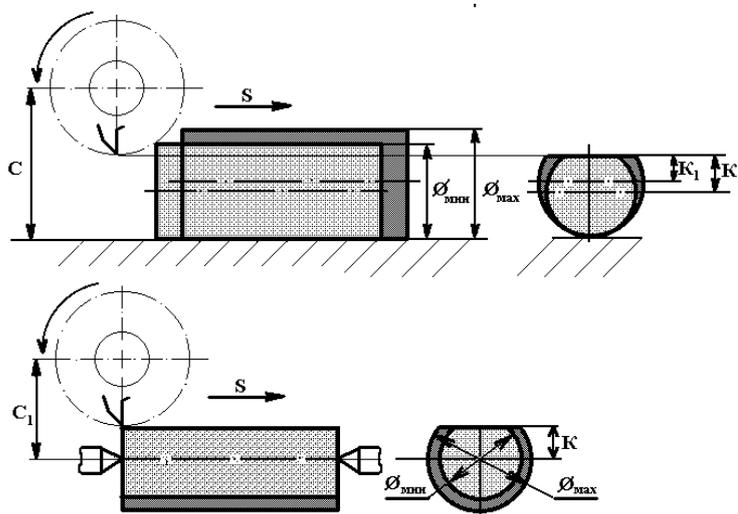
Фрезерование лыски на валу при установке вала на столе станка или в центрах
